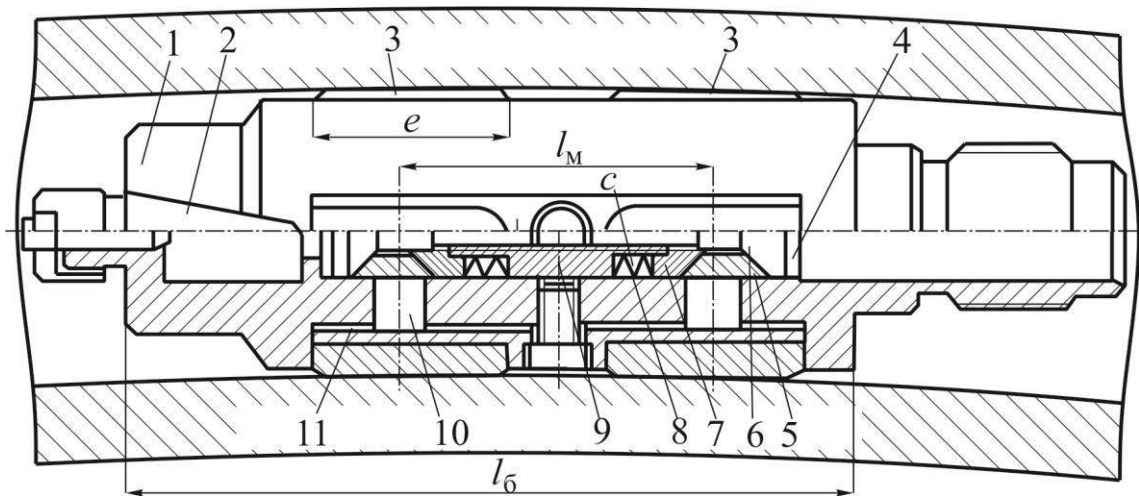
Конструктивна схема розточної головки для обробки гільз гідроциліндрів телескопування:
